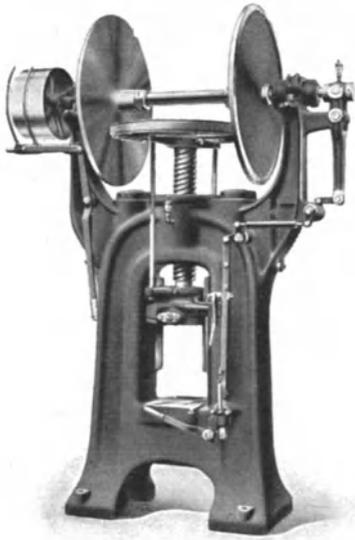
Friktionspresse mit geschlossenem Maschinenkörper für Warmpreßteile.
